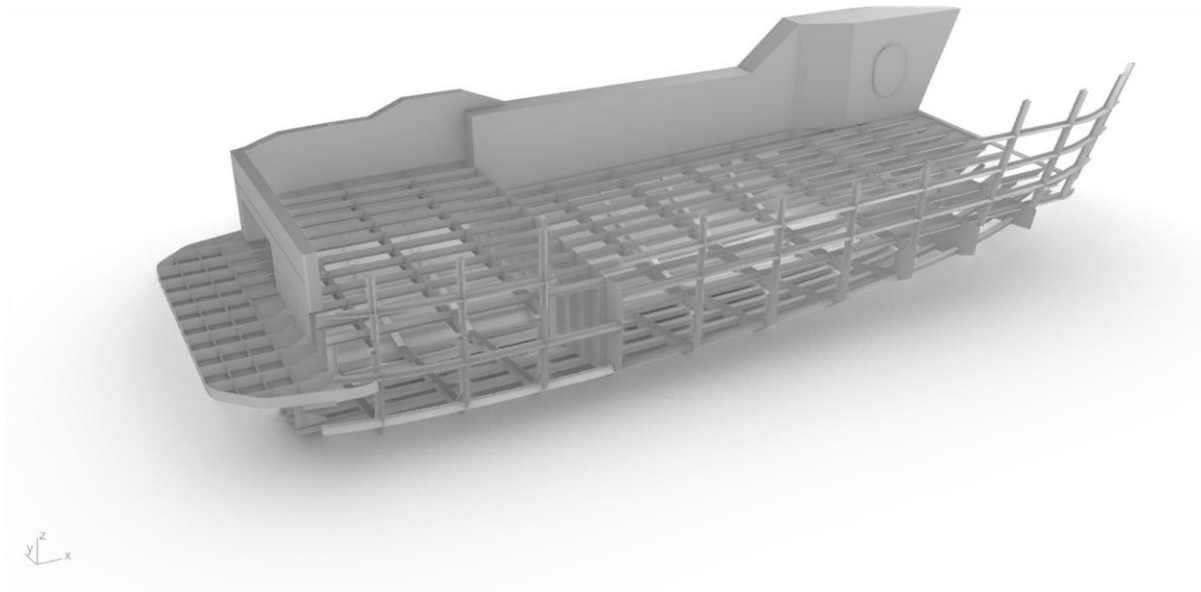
Vista en perspectiva de los elementos estructurales bajo cubierta.
